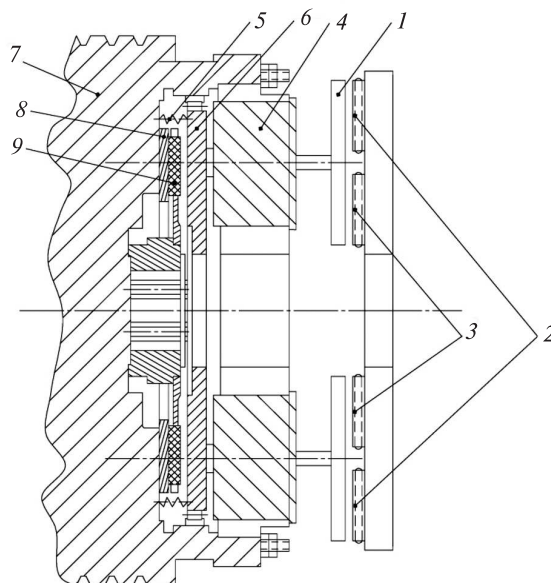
Общая схема орбитального электропривода муфты пресса: 1 — ротор; 2 — обмотка внешнего кольцевого статора; 3 — обмотка внутреннего кольцевого статора; 4 — корпус модуля (см. рис. 1); 5 — пружина; 6 — нажимной диск; 7 — корпус муфты; 8 — опорный диск, который связан с маховиком; 9 — ведомый диск с фрикционными вставками
